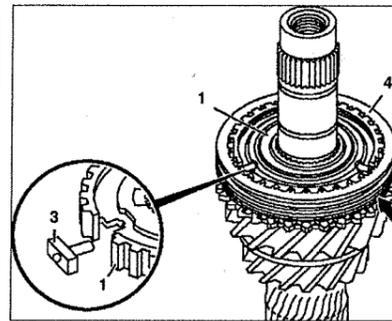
Разборка и сборка механизма включения 3-й и 4-й передач (автомобили с двигателем 611.980):
